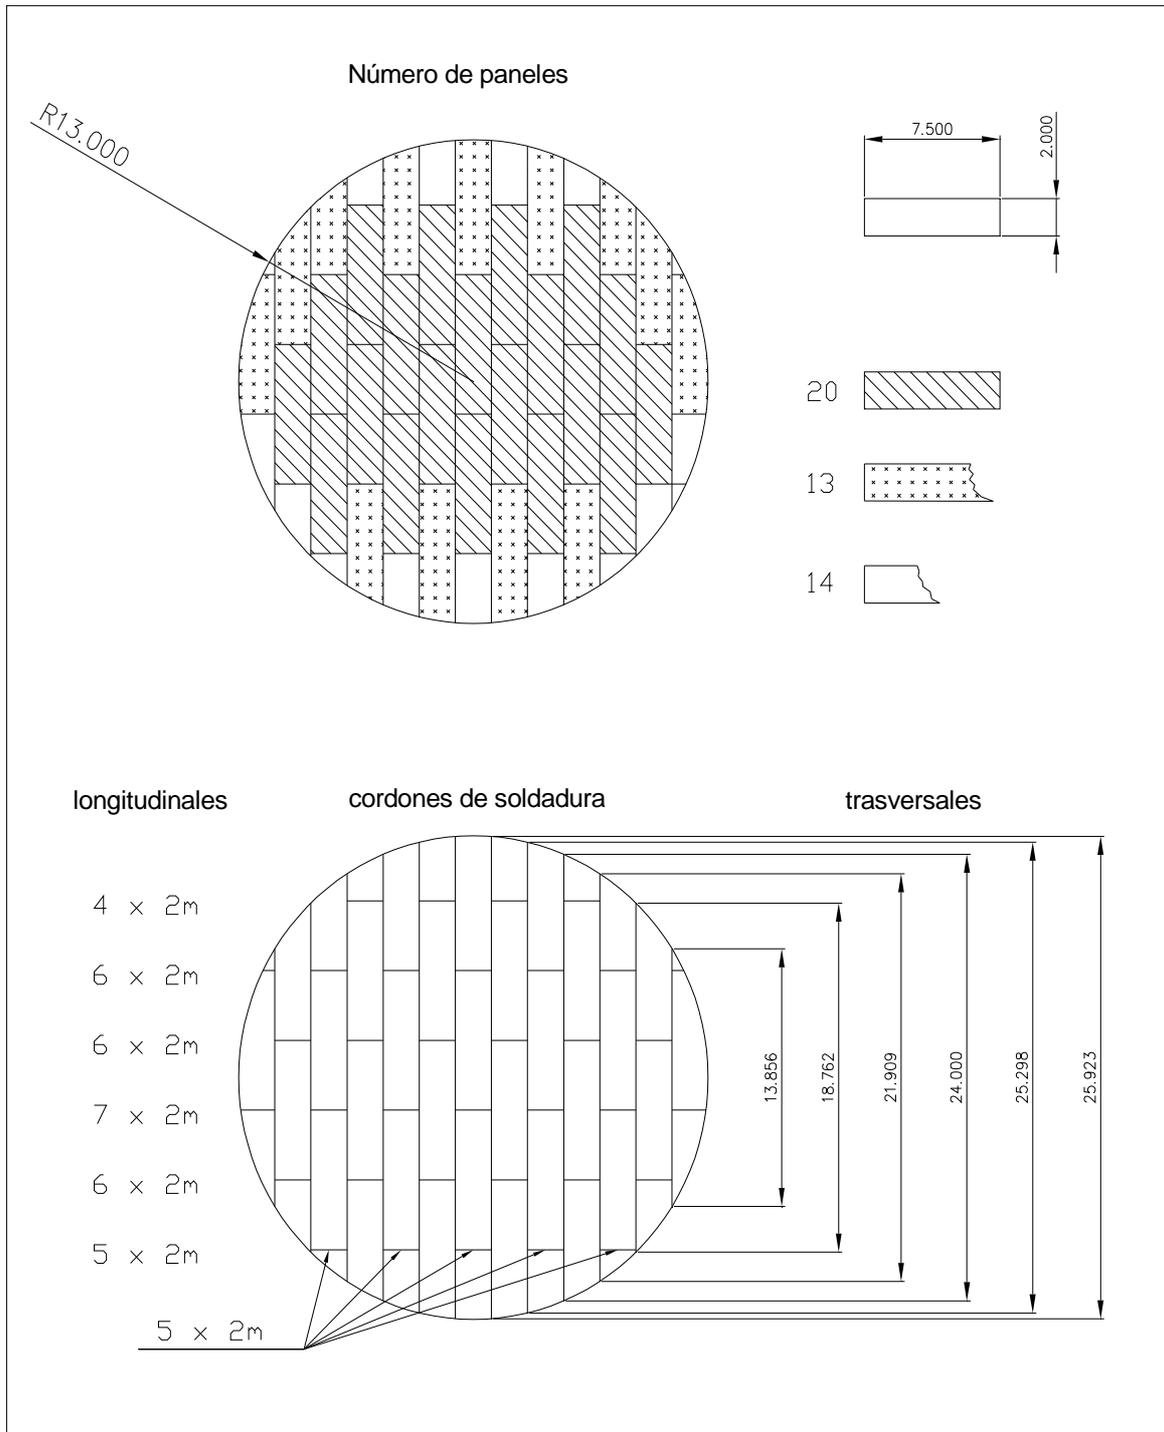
Soldaduras y fondo del tanque N°1 .
